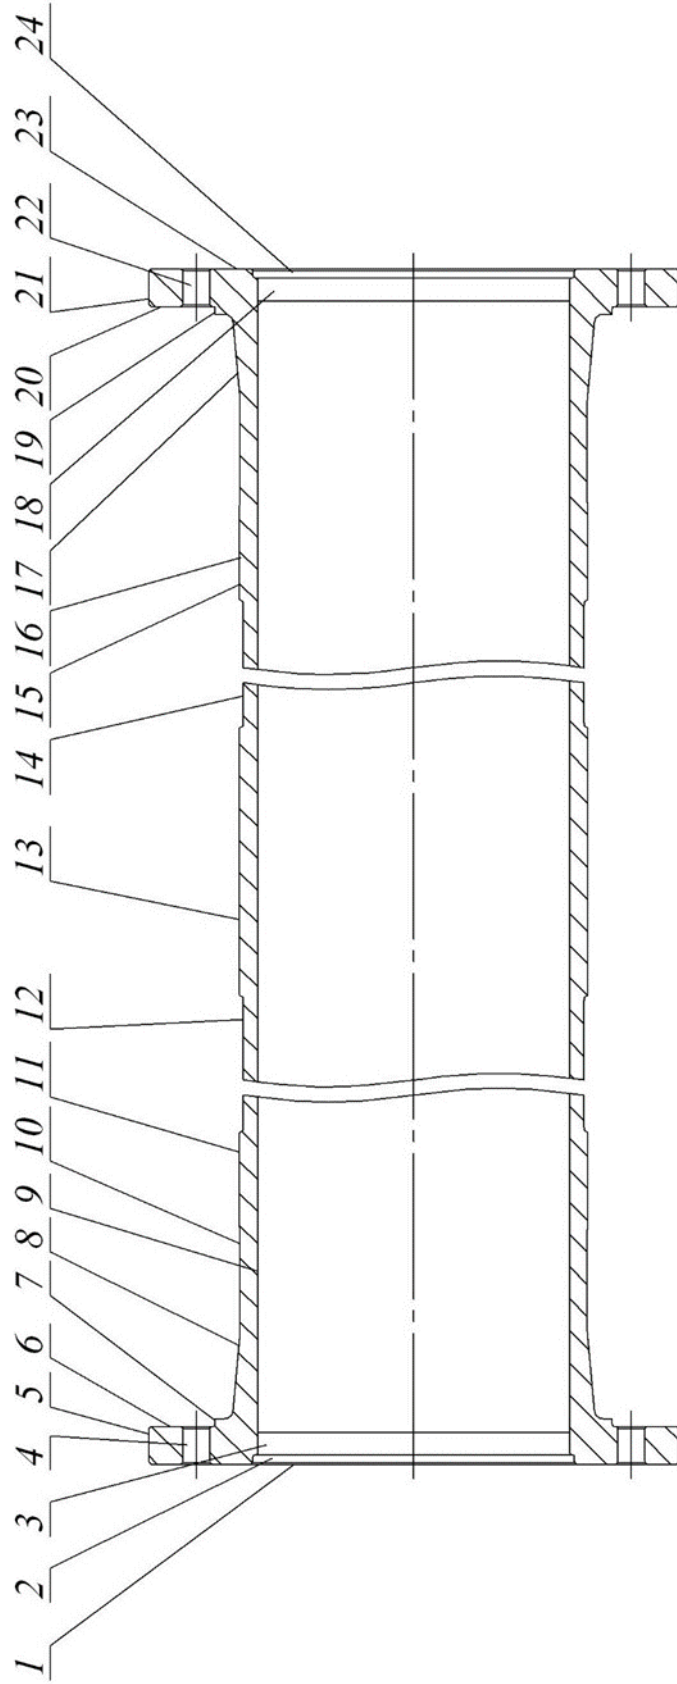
Ескіз вала з нумерацією поверхонь
